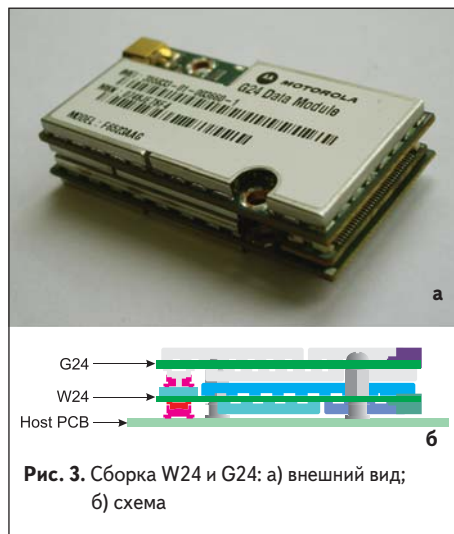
Сборка W24 и G24: а) внешний вид; б) схема
